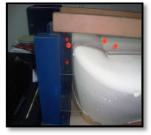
Contact accoudoir/ Siège sur chaîne de montage et désaffleurement de la porte
